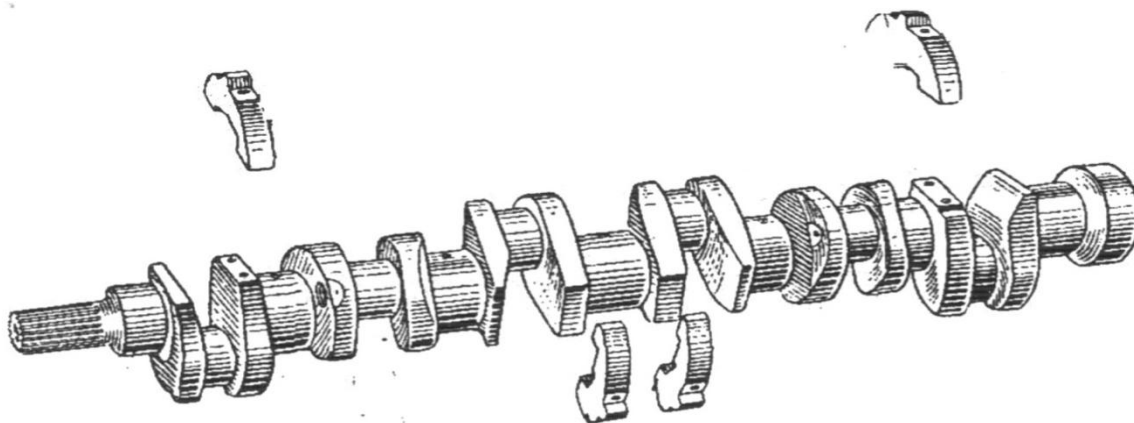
Коленчатый вал двигателя 6Ч13/14
